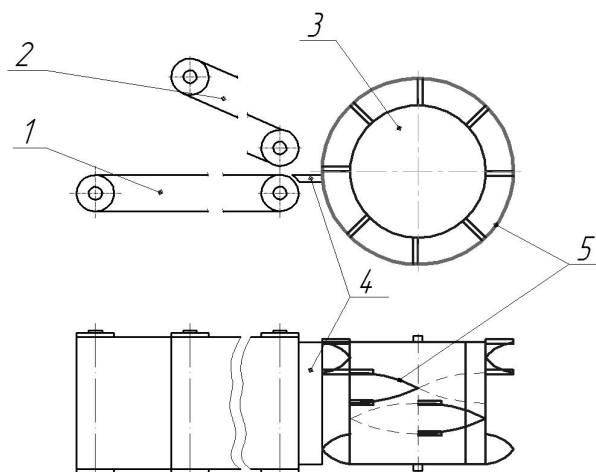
Барабанный режущий аппарат скользящего действия: 1 – подающий транспортер, 2 – подпрессовующий транспортер, 3 – режущий барабан, 4 – противорежущая пластина, 5 – V-образный нож
